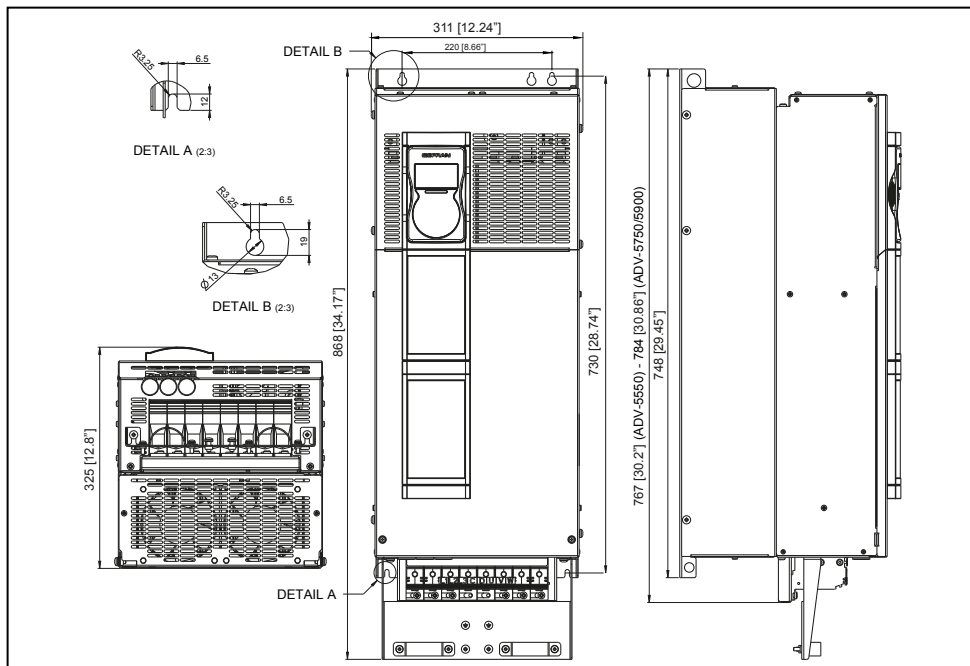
Размеры для типоразмера 5 (ADV200-...-4)
